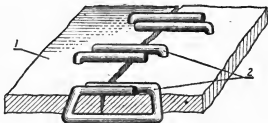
Подготовка тонкостенной детали к заварке трещины с двух сторон:
